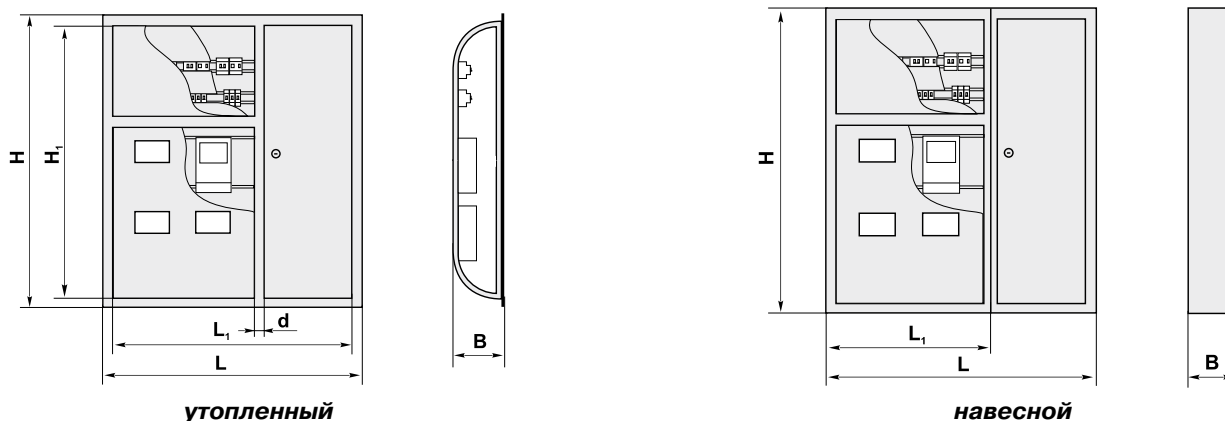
Габаритные размеры щитков серии ЩЭ
